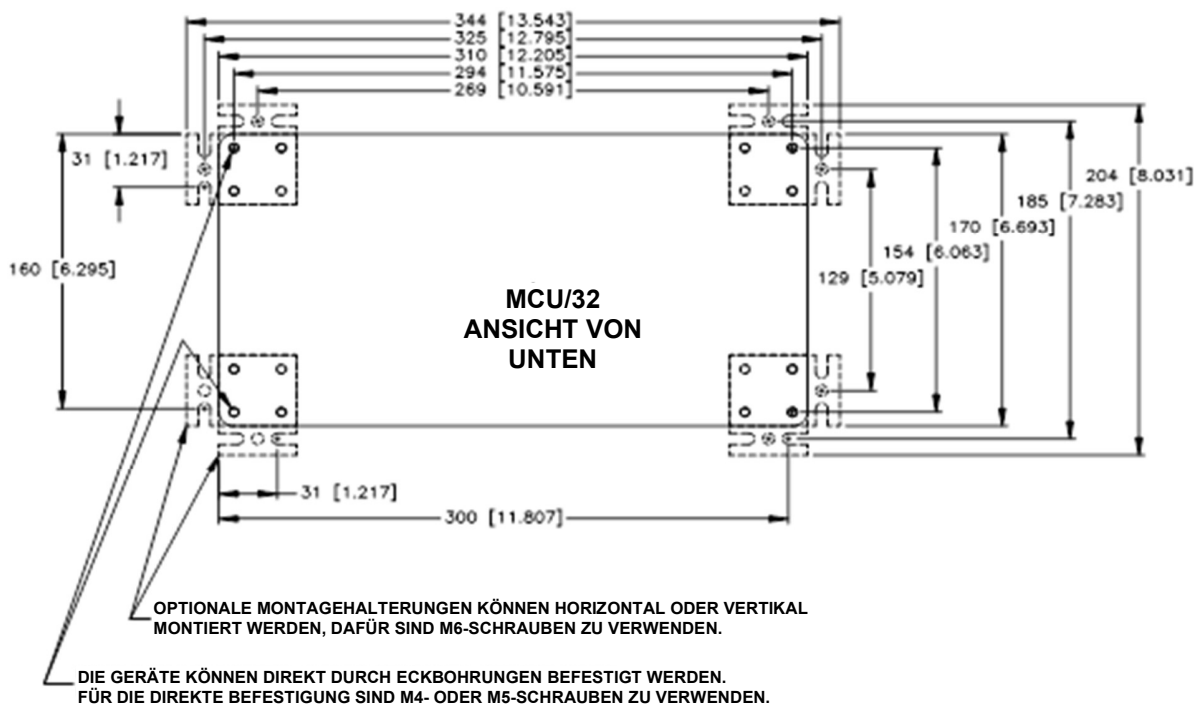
CT24-32 Maßzeichnungen für MCU-Gehäusebefestigung
